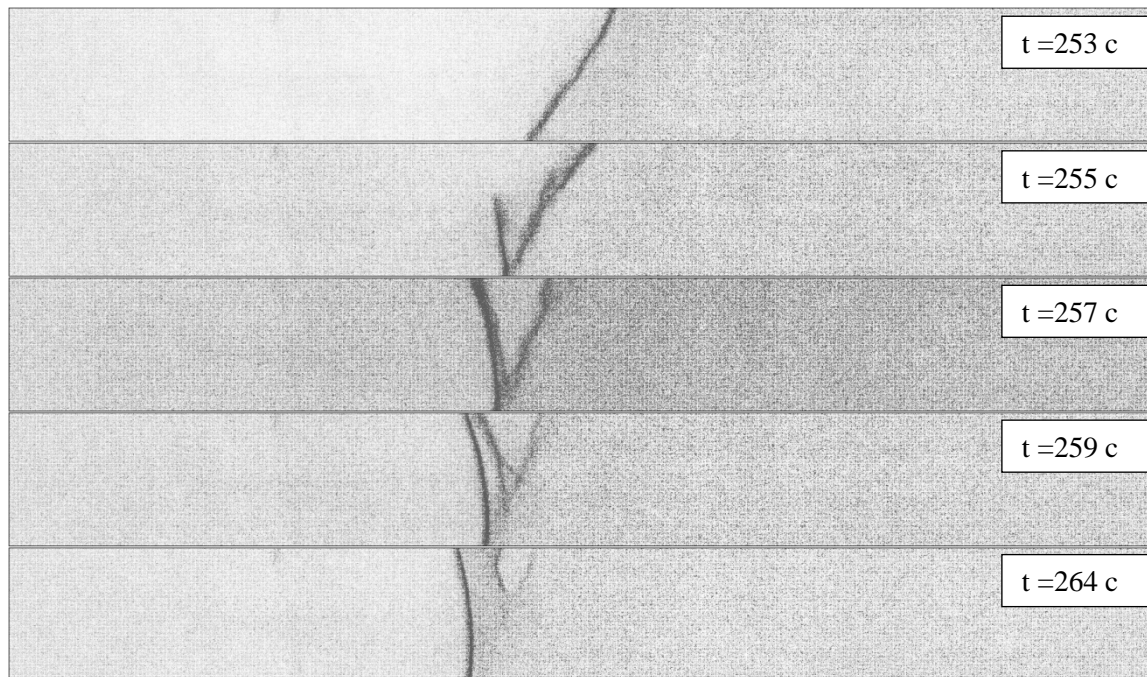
Поведение полос Чернова-Людерса в зонах сварного соединения
